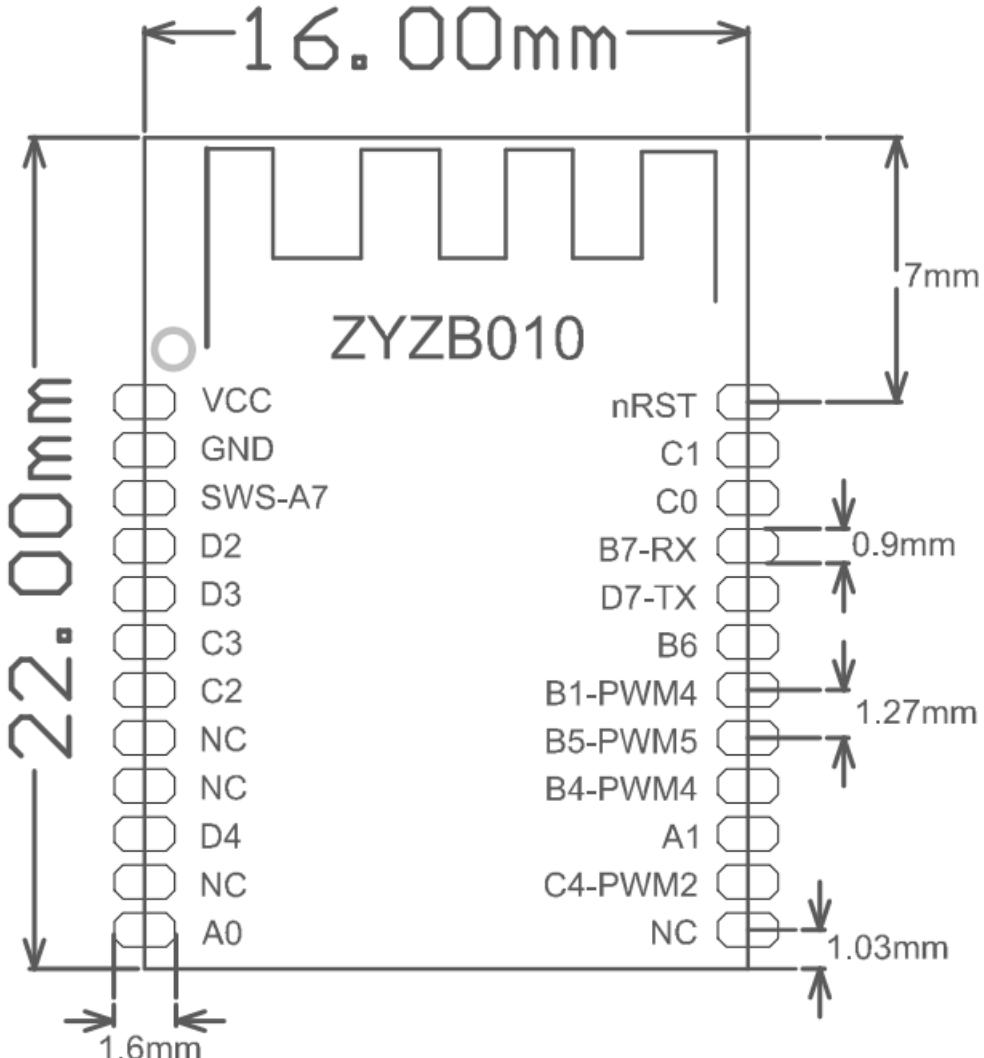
ZYZB010 模组尺寸图 (PCB 厚度 1mm)
